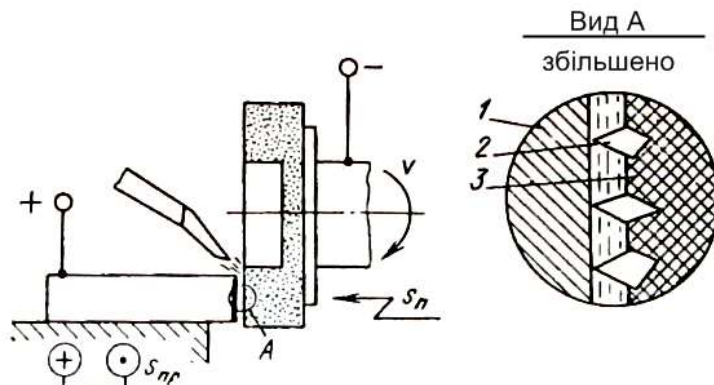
Схема електроабразивного шліфування: 1 – заготовка; 2 – абразивні зерна; 3 – зв'язка шліфувального круга/
